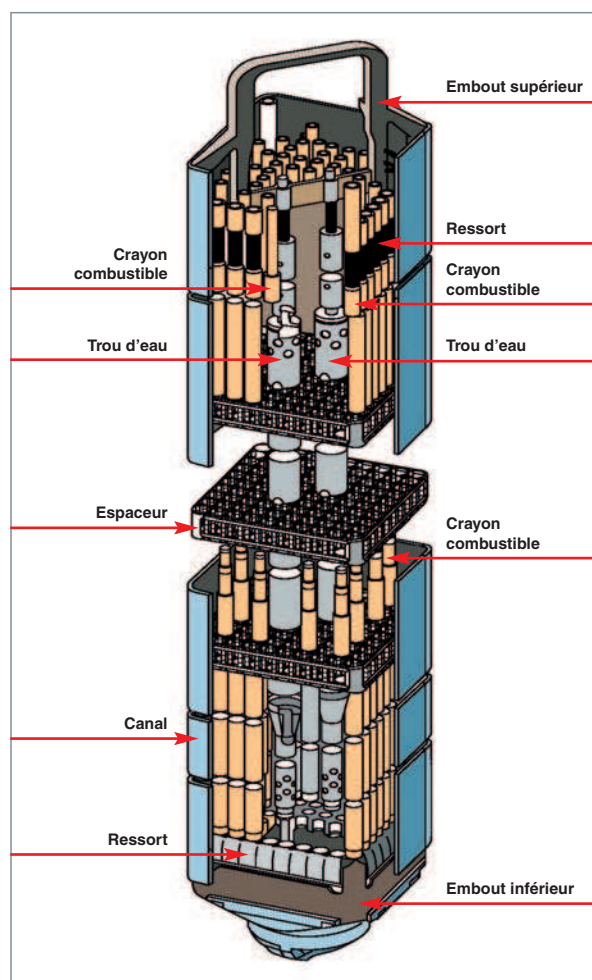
Assemblage combustible pour réacteur à eau bouillante.
